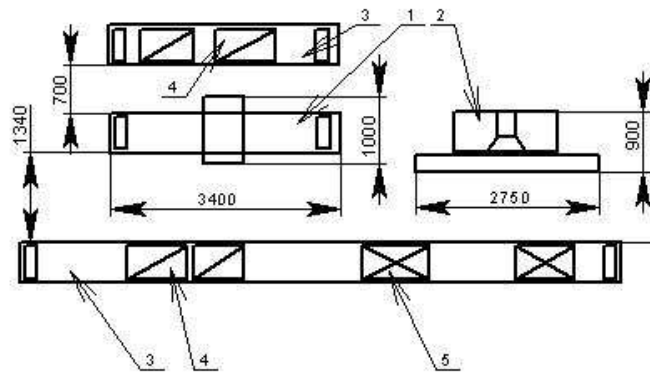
Организация рабочего мест на участке многошпиндельного сверлильного и фрезерного станка
